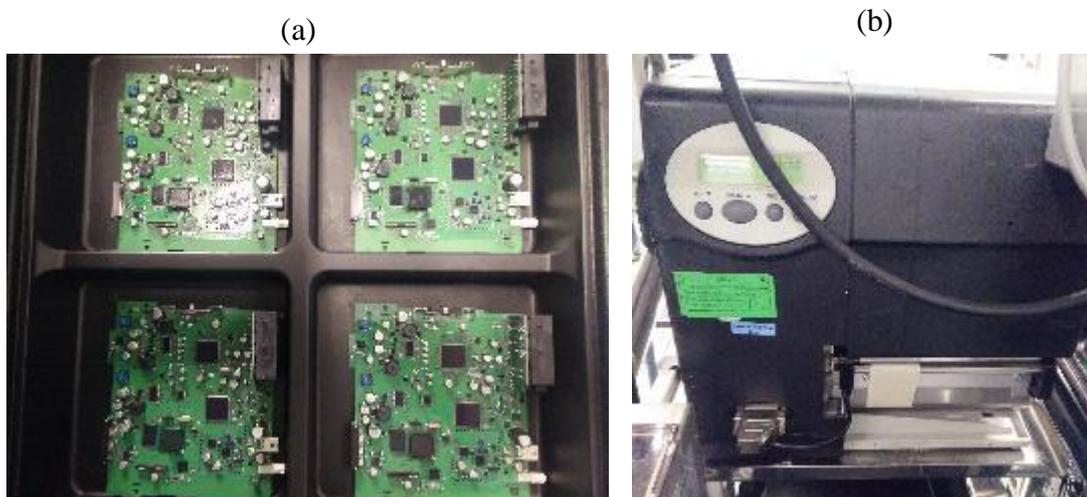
Parts presentation do posto 2: (a) placas principais (b) Impressora
